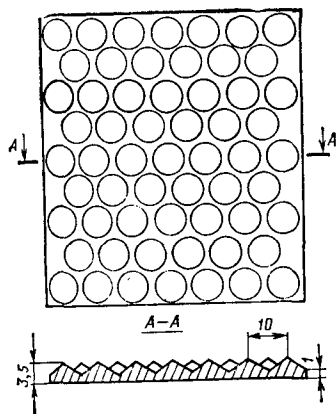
Общий вид резинового коврика с конусообразными выступами (размеры в мм)
